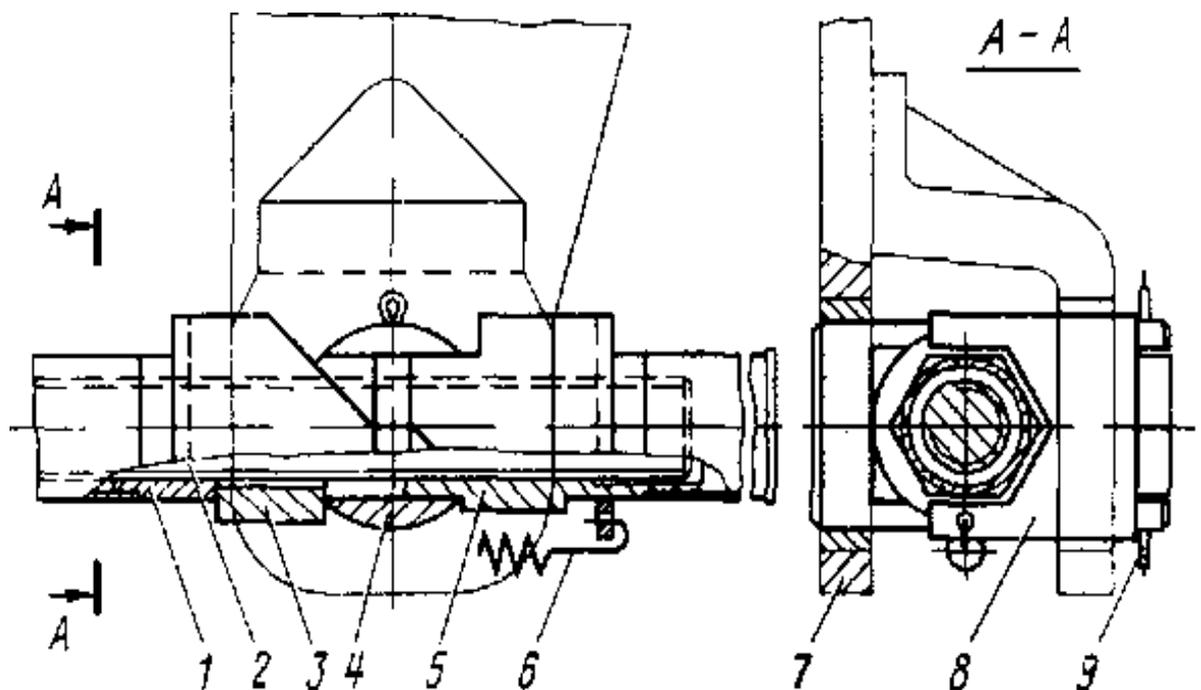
Регулятор выхода штока тормозного цилиндра: 1 – защитная труба; 2 – тяга; 3 – втулка; 4 – палец; 5 - гайка; 6 – пружина; 7 – рычаг; 8 – скоба; 9 – шплинт.
